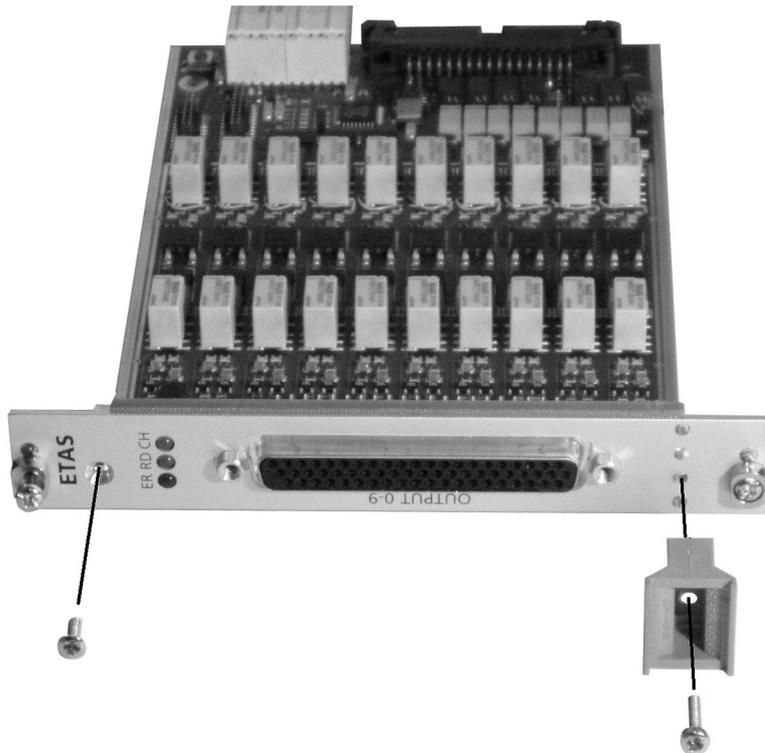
Obere und untere Befestigungsschrauben anbringen
